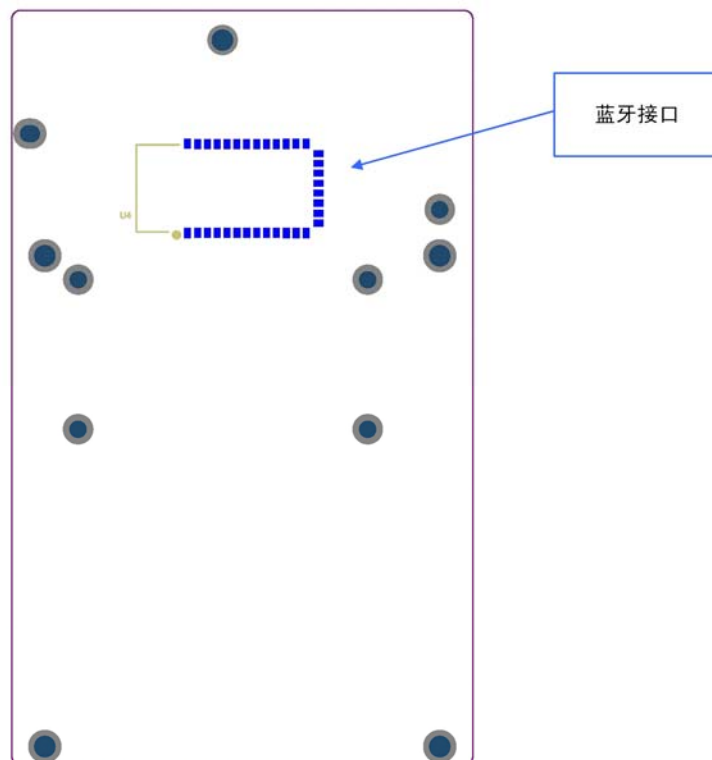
MTP58-FTxx-T1 评估板反面 PCB 丝印
